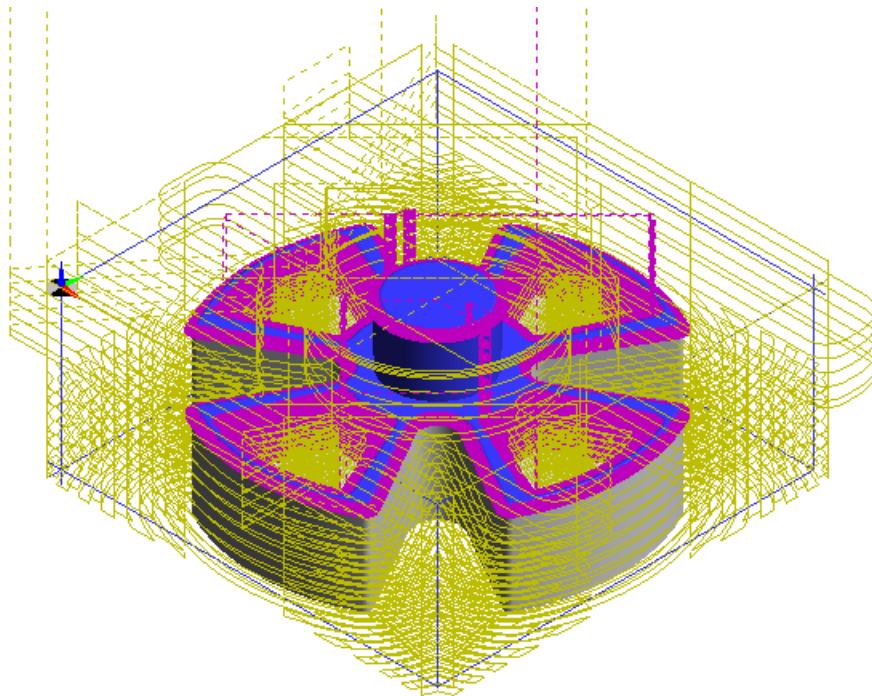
Estratégia de Usinagem para o Centro de Usinagem.
